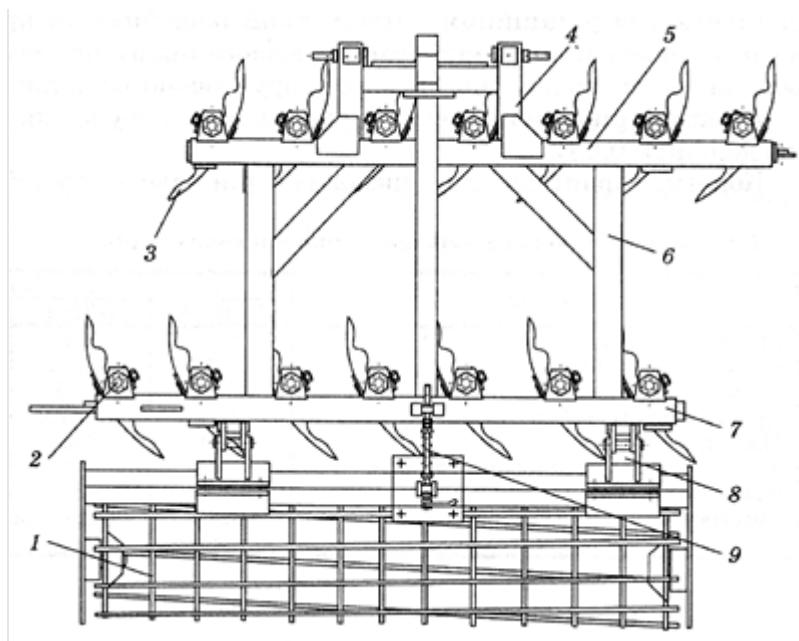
Схема дискатора: 1 – коток; 2, 3 – дискові стояки; 4 – начіпний пристрій; 5 – передня балка; 6 – повздовжна балка; 7 – поперечна балка; 8 – причепний пристрій котка; 9 – механізм регулювання занурення.
